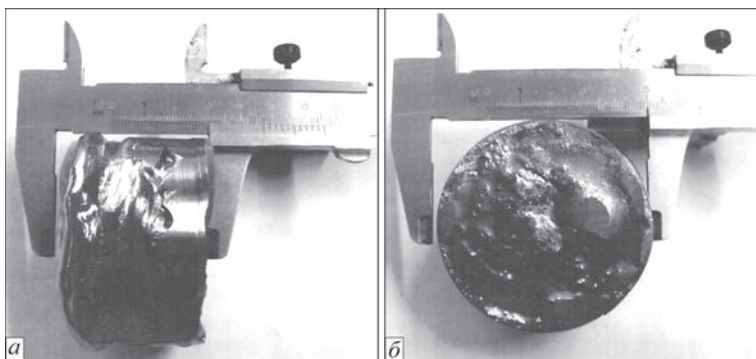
Внешний вид детали с формой тела вращения: а — вид сбоку; б — вид снизу
